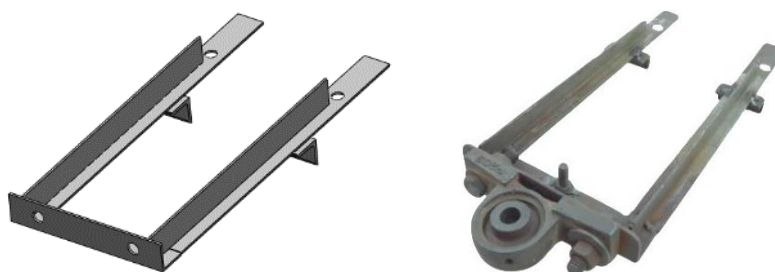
Diseño y construcción del soporte para rodamiento de brida.
